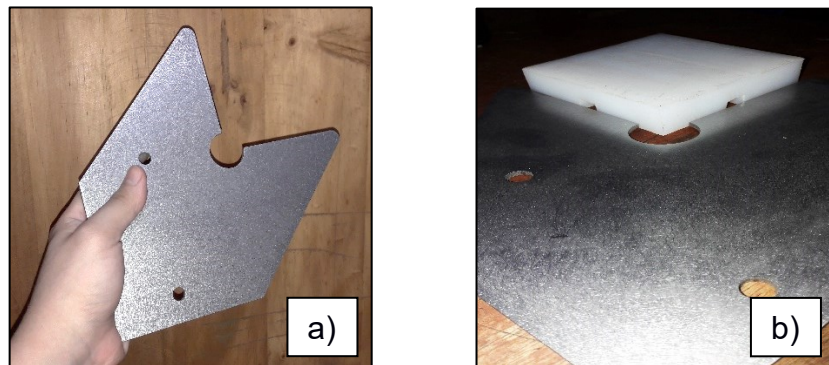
Plantilla de centrado: a) Perspectiva b) Detalle de acceso a esquina.
